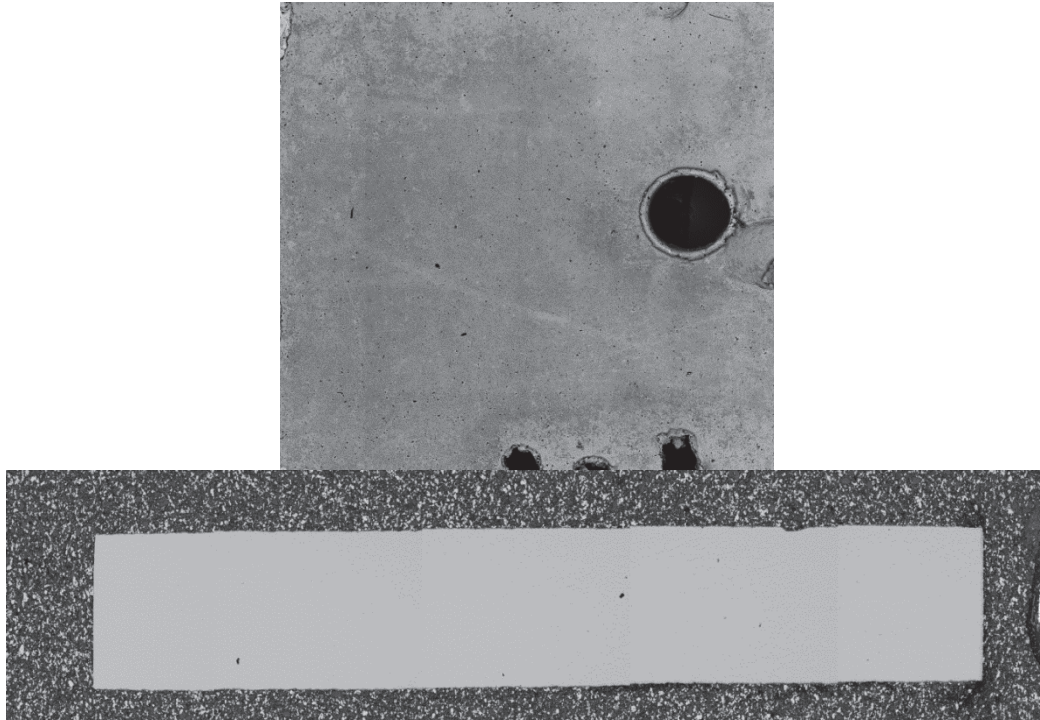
Vue d'ensemble (surface corrodée (a)) et coupe transversale (b)) d'un coupon métallique analysé.
